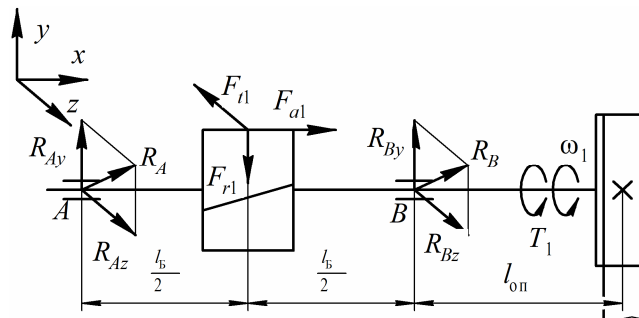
Пример расчетной схемы быстроходного вала цилиндрического одноступенчатого редуктора
